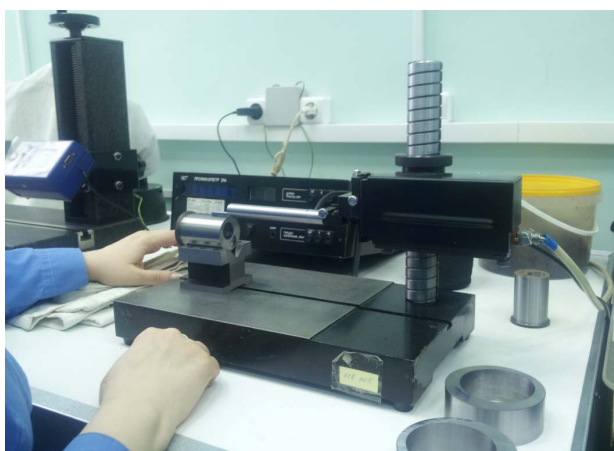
Профилометр цеховой 296 фирмы «АСМА-Прибор» для контроля шероховатости
